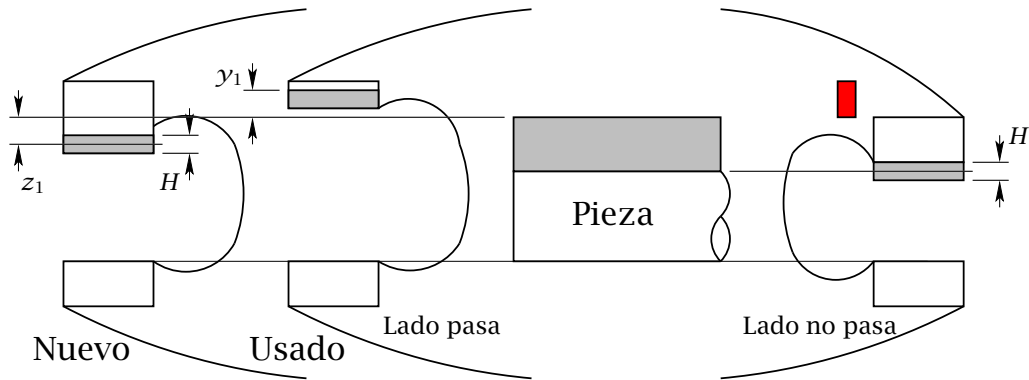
Límites de tolerancia de un calibre de herradura.
